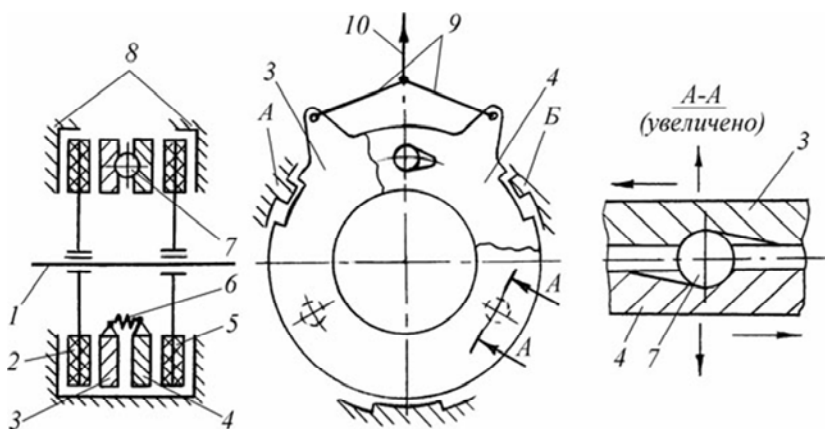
Схема закрытого дискового тормоза с сервоусилением
